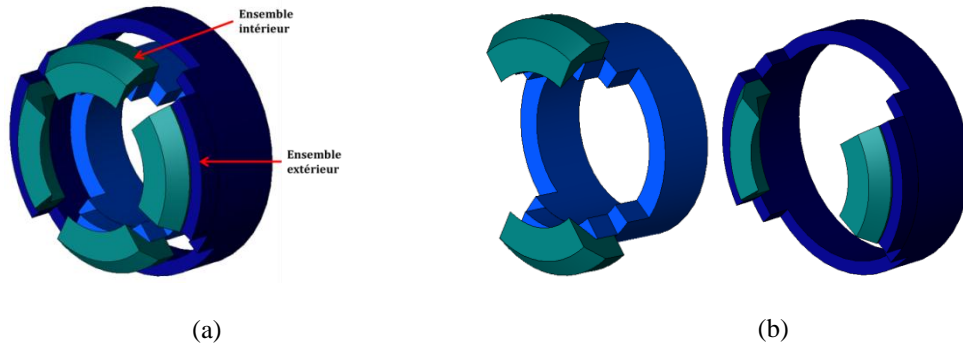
Vue des ensembles rotoriques assemblés (a) et séparés (b)
